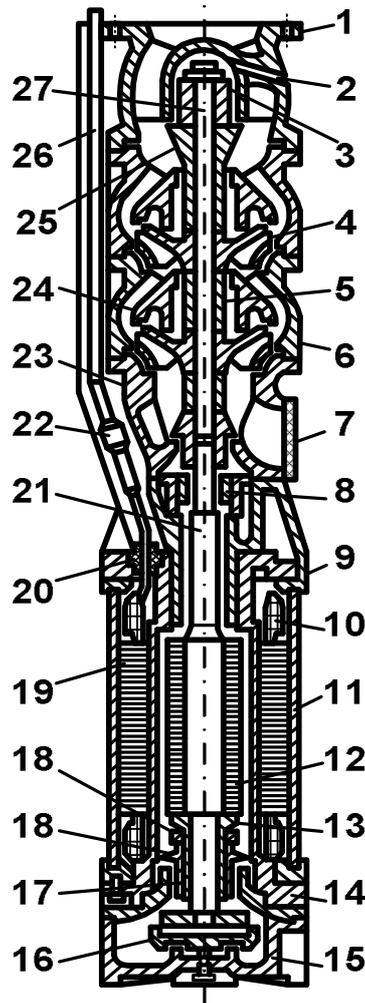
Насос типа ЭЦВ: 1 – напорный фланец; 2 – дренажный канал; 3 и 8 – верхний и нижний радиальные подшипники насоса; 4 – рабочее колесо; 5 – дистанционная втулка; 6 – секция корпуса с направляющим аппаратом; 7 – фильтрующая решетка; 8 и 17 – верхний и нижний радиальные подшипники двигателя; 9 – проставка; 10 – обмотки возбуждения; 11 и 14 – наружная и внутренняя оболочки статора; 12 – ротор; 13 – упорная втулка; 15 – нижний фланец; 16 – упорный подшипник; 18 – уплотнение; 19 – статорное железо; 20 – изолятор; 21 и 27 – валы двигателя и насоса; 22 – электрический разъем; 23 – всасывающая секция; 24 – обтекатель; 25 – втулка-обтекатель; 26 – высоковольтный кабель.
